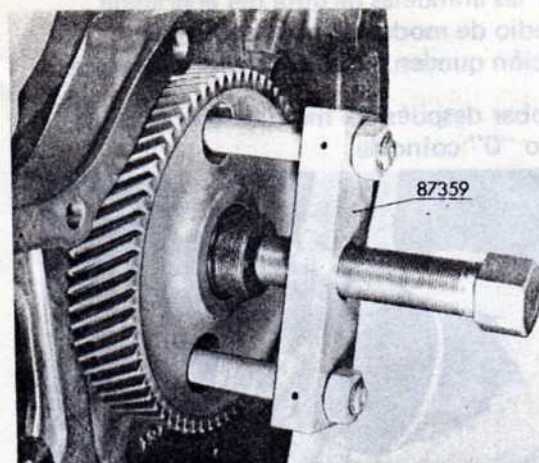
Extractor para el engranaje de la bomba y el engranaje del árbol de levas.
